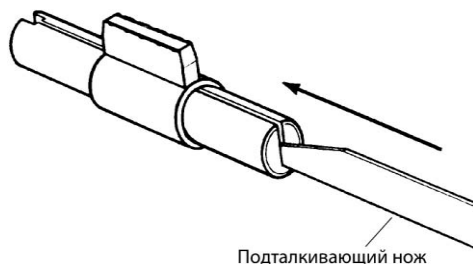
Поверните корпус цилиндра (С разрешения компании Schlage Lock Company)
